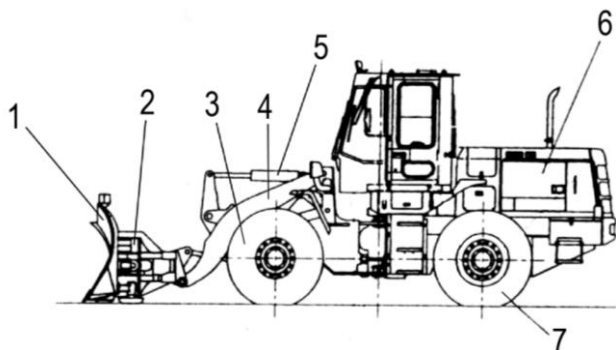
Схема конструкции снегоуборочного бульдозера:
